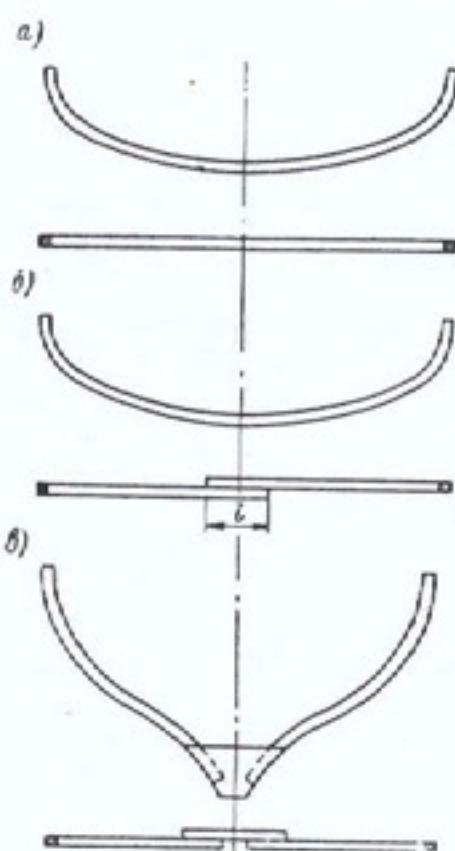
Схема конструкции гнутого шпангоута: а — из одного бруска; б — из двух брусков с перекроем в ДП; в — с соединением на флоре.
